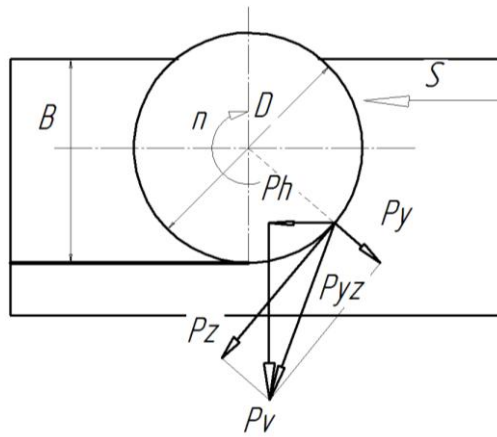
Схема взаємодії кінцевої фрези та матеріалу заготовки з пластмаси при несиметричному попутному фрезеруванні :  $P_v$  – сила різання, що діє нормально до поверхні заготовки;  $B$  – ширина зрізаємого шару;  $D$  – діаметр фрези;  $\Delta l$  – величина пружних відтискань поверхні заготовки;  $S$  – подача верстата
